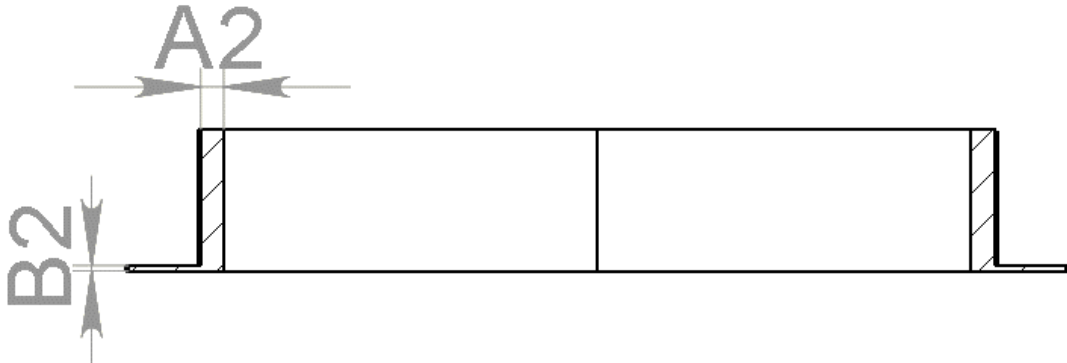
Розміри верхньої частини корпусу підшипникового вузла валу шківів змінного моменту інерції, які змінювались під час вагового покращення
